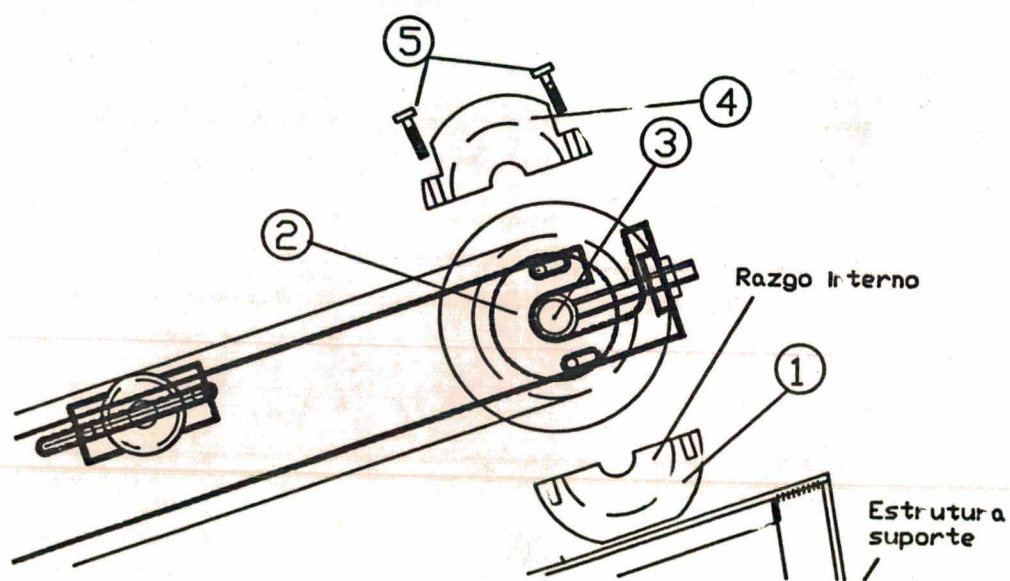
Detalhe da montagem do conjunto da correia transportadora inferior, na estrutura suporte
